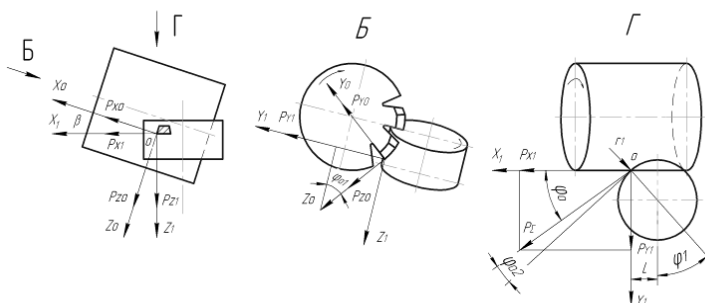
Составляющие силы резания, действующие на инструмент и заготовку в процессе зубофрезерования [2]
